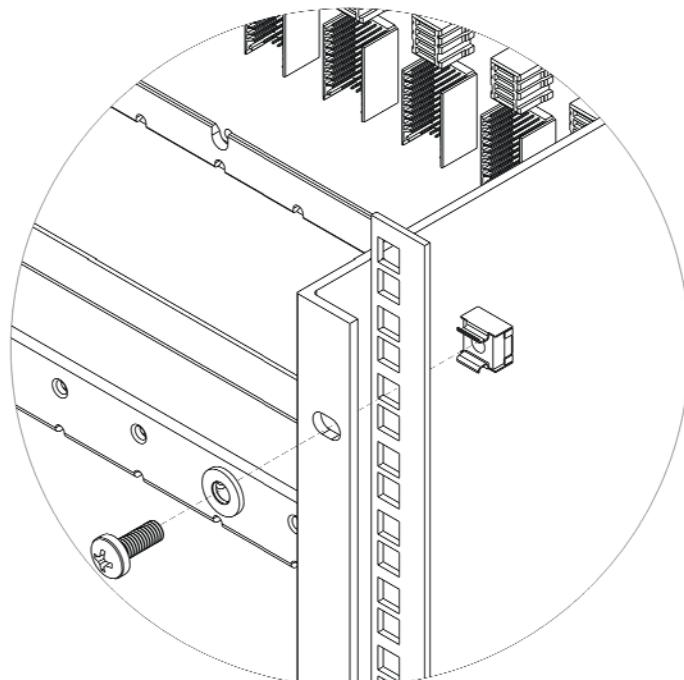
Fixação do suporte básico X-BASE PLATE 15 02
